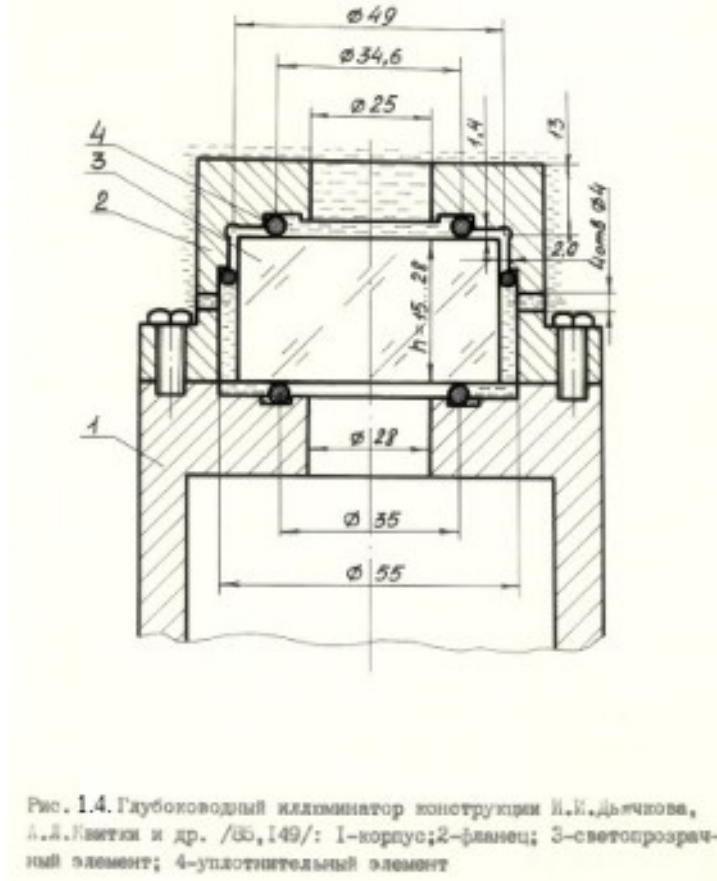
Предназначенный для высоких давлений иллюминатор конструкции И. И. Дьячкова, А. Л. Квитки и др. [85, 149]: 1 – корпус; 2 – фланец; 3 – светопрозрачный элемент; 4 – уплотнительный элемент.
